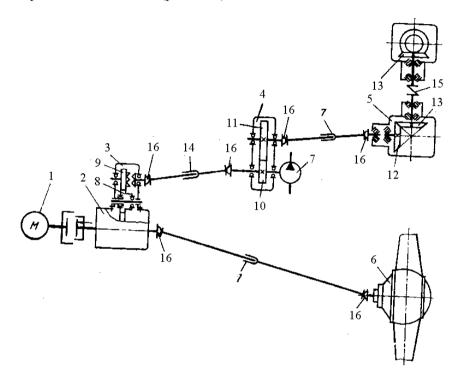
Кинематическая схема механической трансмиссии ходовой части и одного из исполнительных механизмов автомобильного крана:
